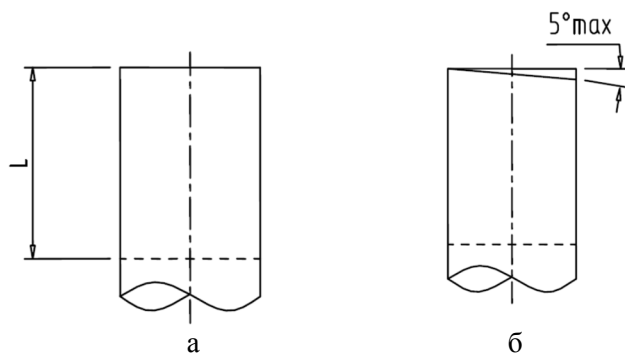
(а,б) - Установка трубки в фитинг
